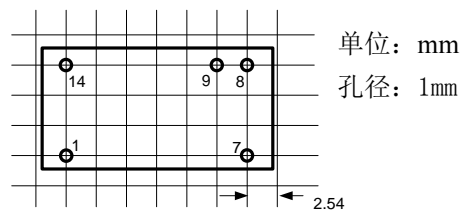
ZY_BKD-1W 外观机械尺寸、建议 PCB 版图
